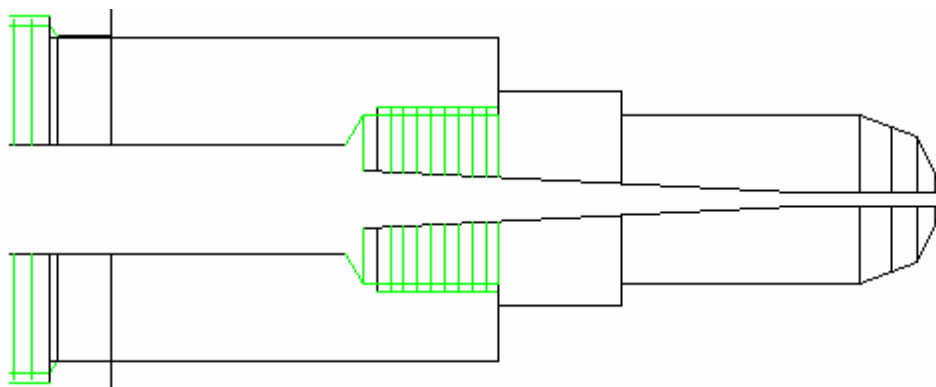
Ensamble de Boquilla y Cámara de inyección.
